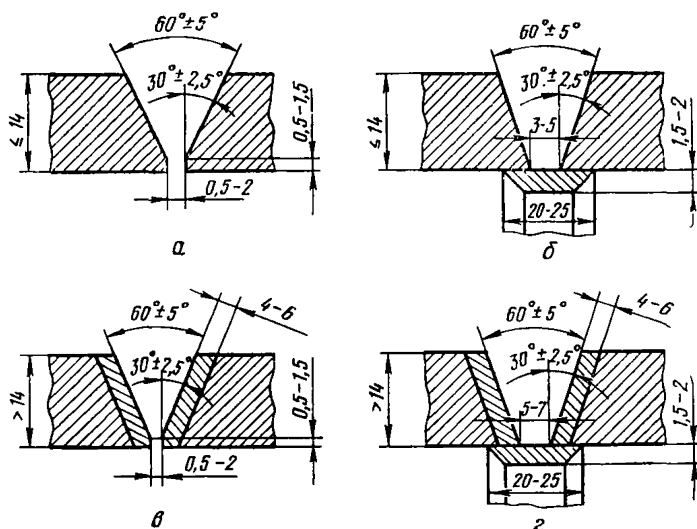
Подготовка кромок и сборка под сварку:
